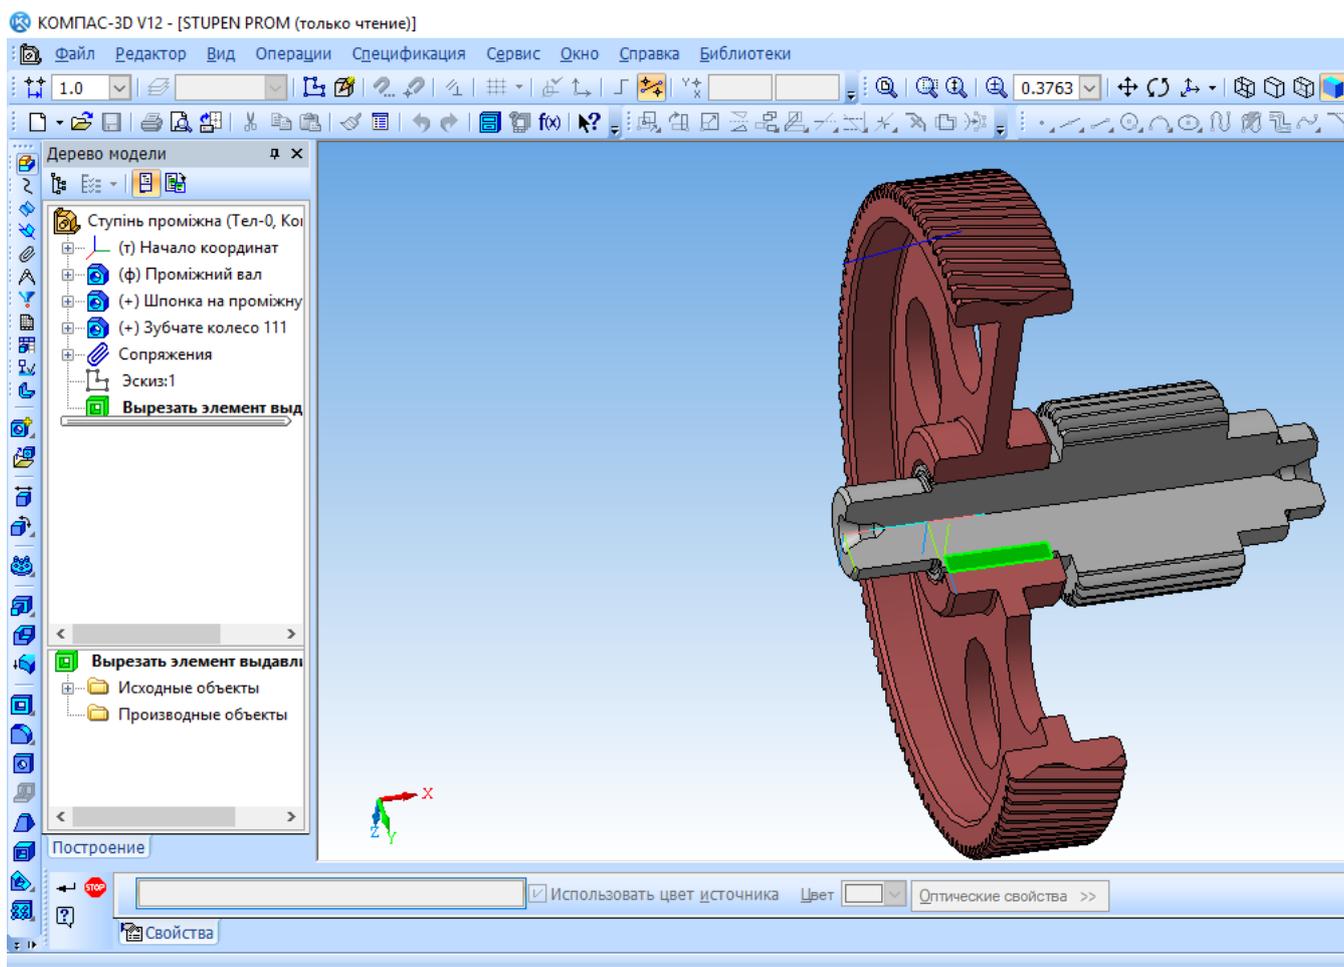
3D сборка промежуточной зубчатой передачи с вырезом $\frac{1}{4}$ части
